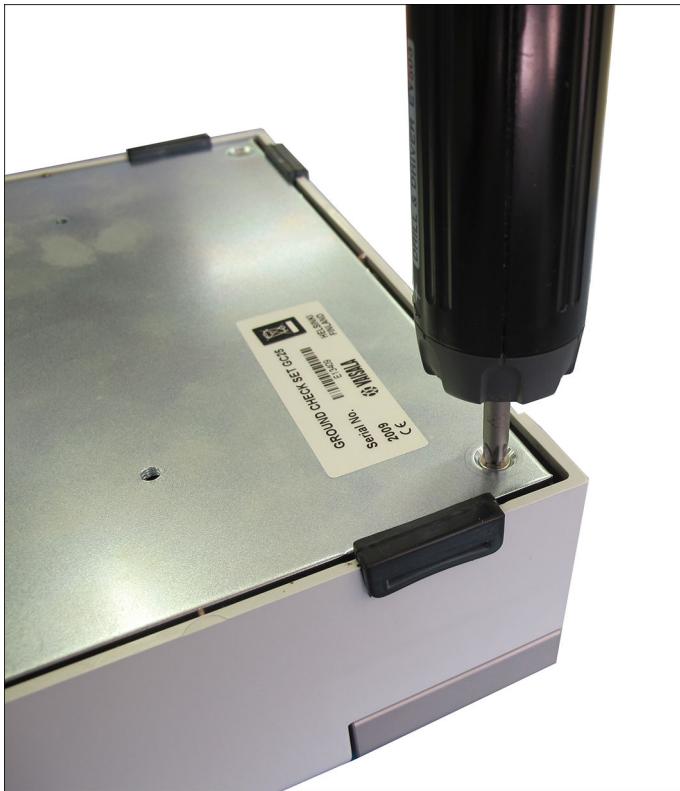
Schrauben der hinteren Abdeckung ausbauen
